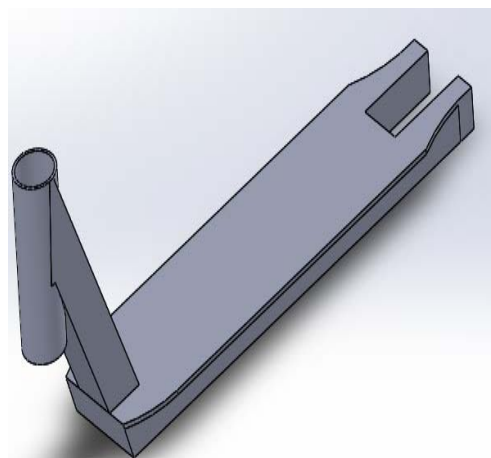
Diseño del cilindro por el que se ensambla la horquilla de dirección.
